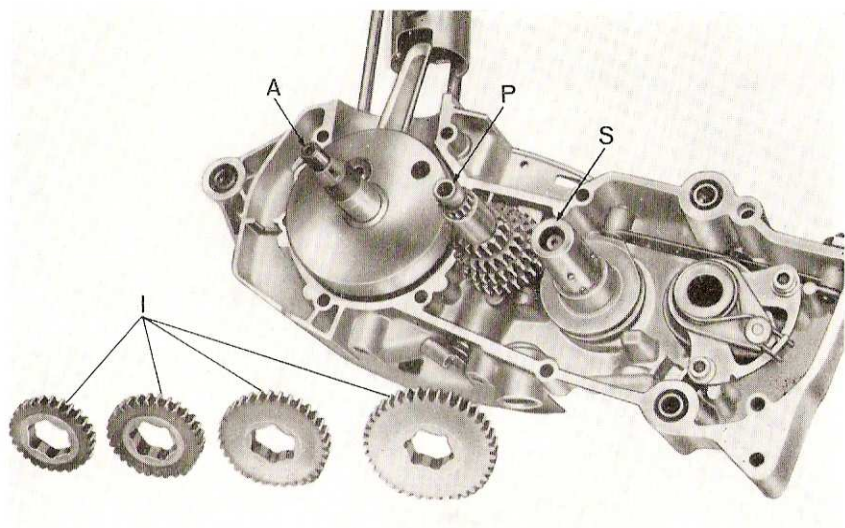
Montage de l'arbre moteur et du changement des vitesses
